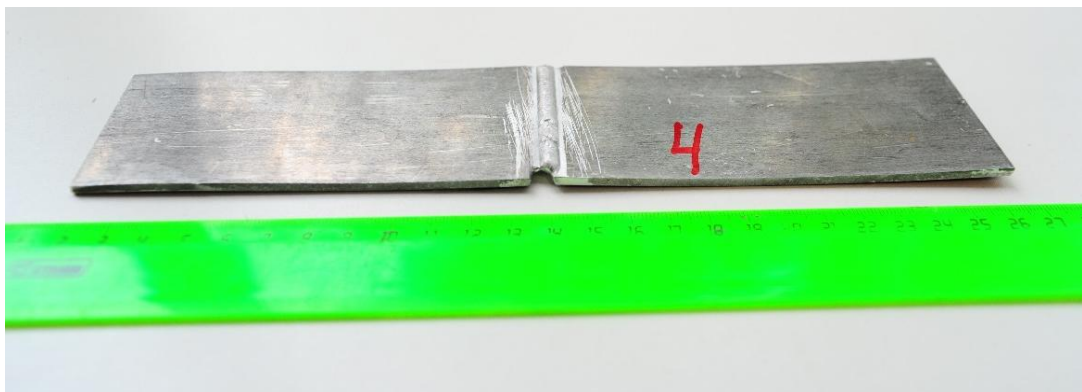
Сварная заготовка со стороны сварного шва
